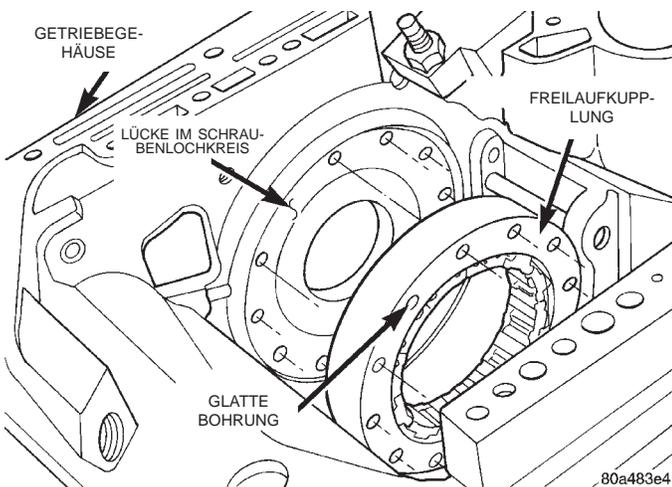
Klemmring der Freilaufkupplung ausrichten
